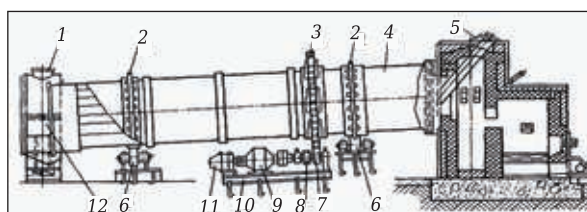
Вращающаяся печь: 1 — патрубок; 2 — бандаж; 3 — венцовая шестерня; 4 — сварной стальной цилиндр; 5 — загрузочный питатель; 6 — опорный ролик; 7 — подвенцовая шестерня; 8 — зубчатая пара; 9 — редуктор; 10 — сварная плита; 11 — электродвигатель; 12 — разгрузочная камера
